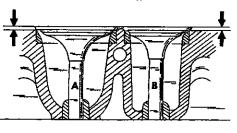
Головка клапана должна располагаться ниже повержности головки цилиндров на размер, указанный стрелками. Размеры для впускных клапанов "А" и для выпускных клапанов "В" не одинаковы.
